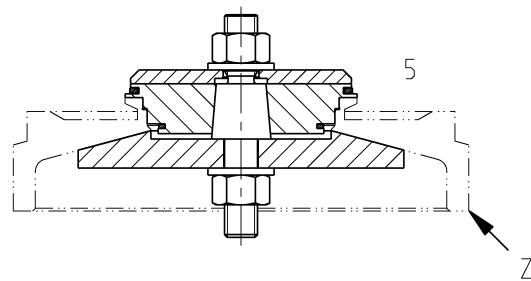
5=Schweißvorrichtung für Gehäuseanschluss T-S / Z=Schweißung
